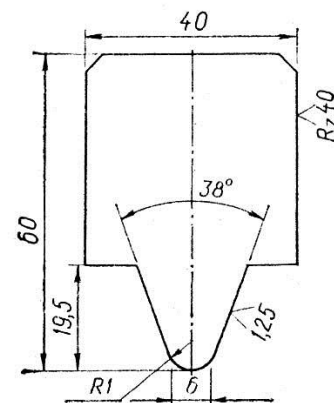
Шаблон для вимірювання профілю канавки шківів вентилятора і натяжного ролика двигуна.
